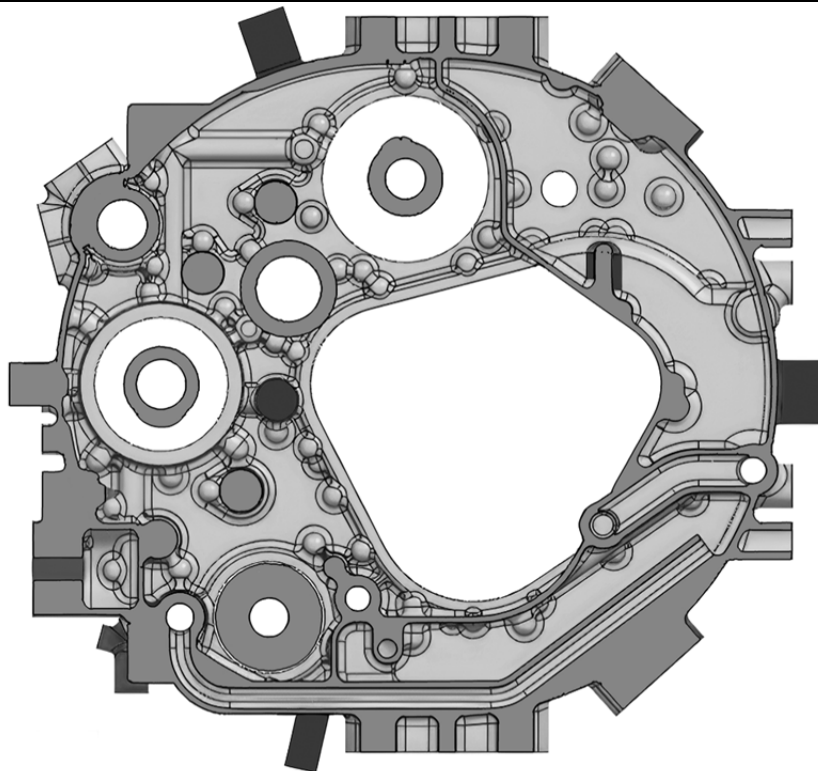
Корпус редуктора (3D-модель отливки в разрезе)
